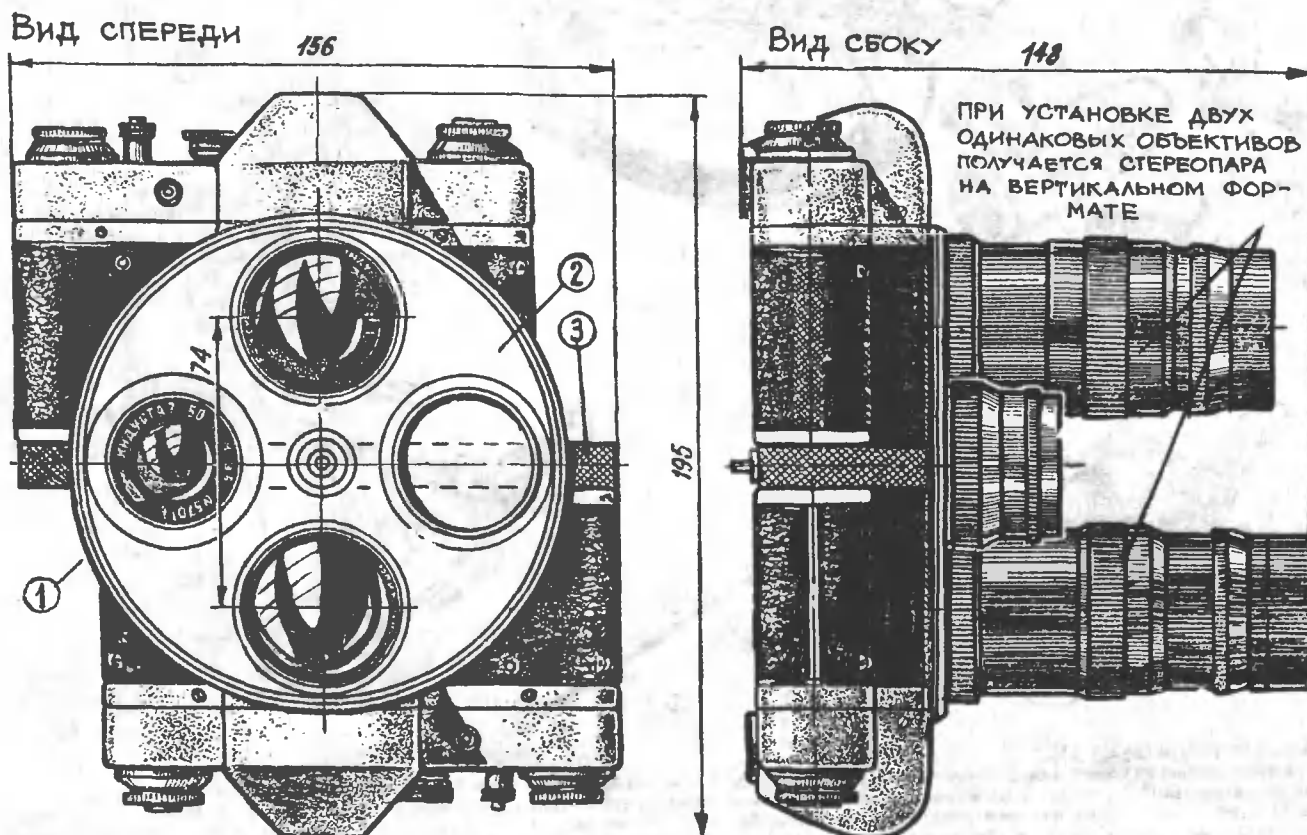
Вид спереди и вид сбоку и детализовка фотоаппарата «Победа» (названия деталей 1, 2, 3 см. в подписи к рис. 2).
